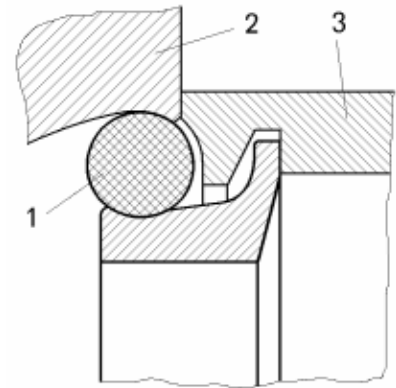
Установка торцового резинометаллического уплотнения в гнездовое отверстие:
